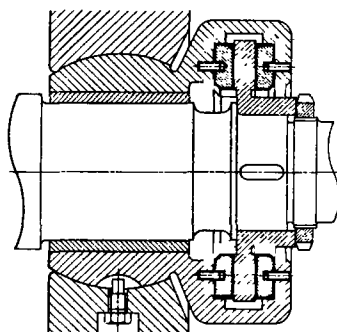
Самоустанавливающийся сегментный подшипник двустороннего действия
